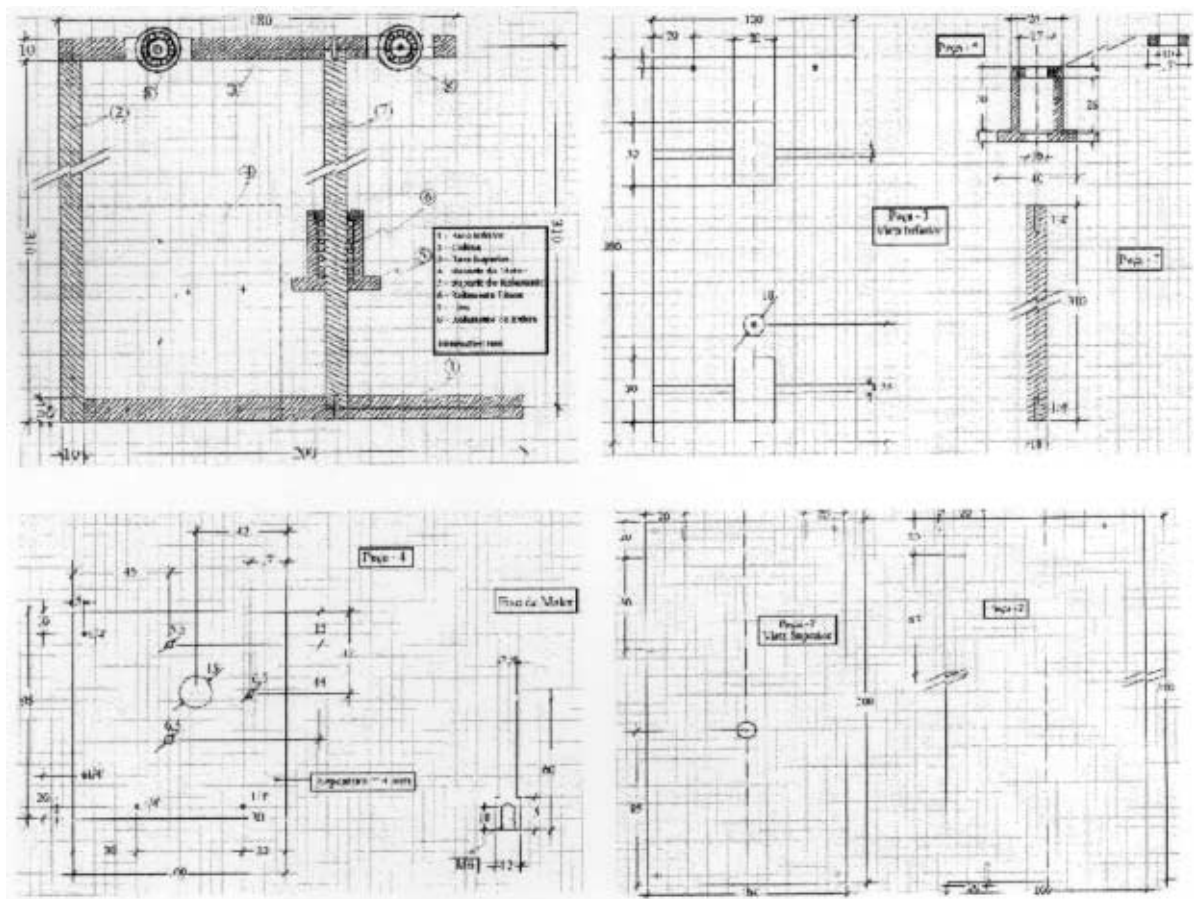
Desenho técnico, com detalhes, do *dip coating* construído.
